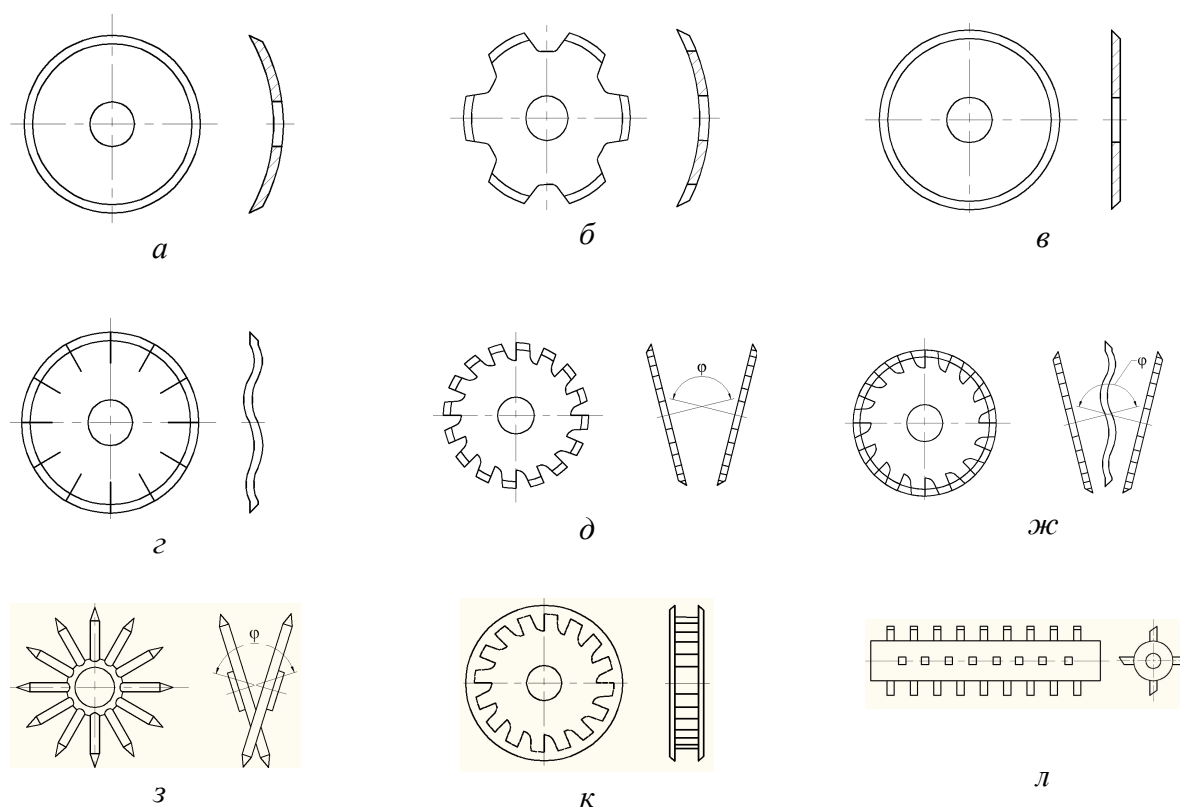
Самопривідні робочі органи: а – сферичний диск; б – сферичний вирізний диск; в – плоский диск; г – рифлений дисковий ніж; д – дисковий ножовий щілиноріз; ж – комбінований щілиноріз; з – голчастий дисковий щілиноріз; к – фреза з дисковим ножами; л – роторна борона
